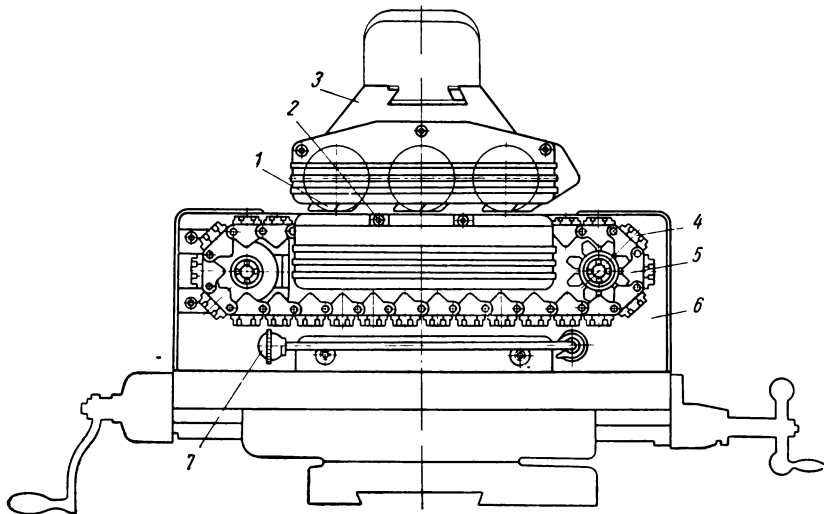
Приспособление для непрерывного фрезерования шлицев в корончатых гайках с индексированием в процессе работы
